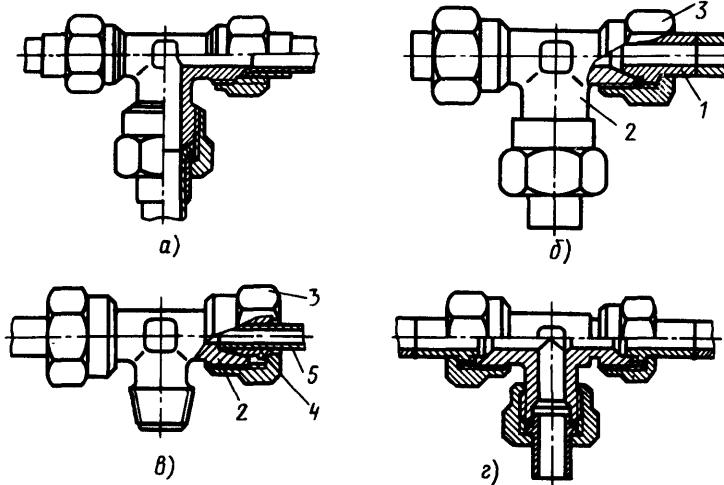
Соединение (а—г) жестких трубопроводов
